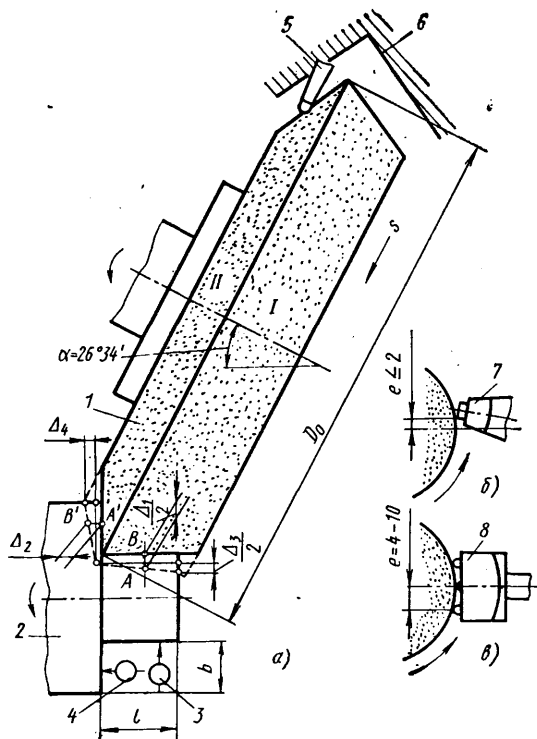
Схема правки абразивного круга и работы торцекуруглошлифовального станка
